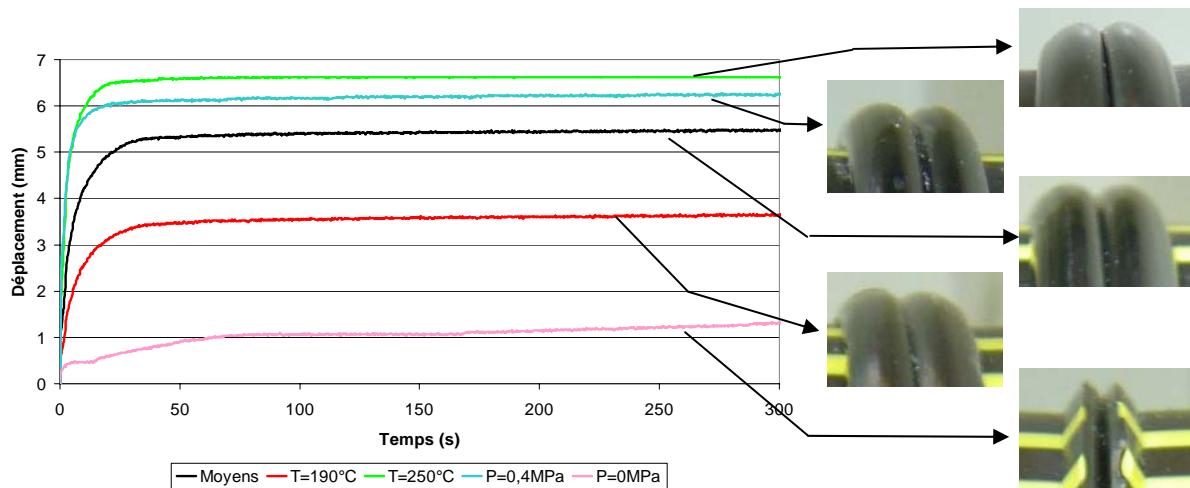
Déplacement au cours de la phase de soudage en fonction des paramètres de soudage et allure du bourrelet résultant de chaque type de soudage
